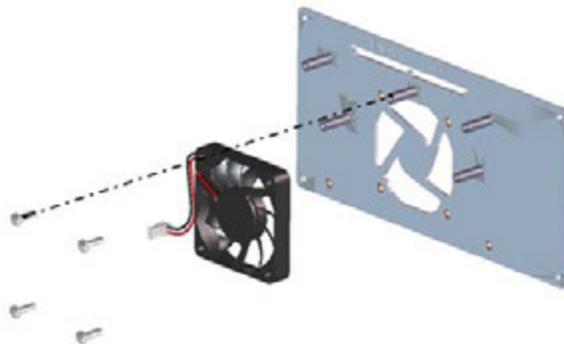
Extracción de los cuatro tornillos y el ventilador de la placa del ventilador
